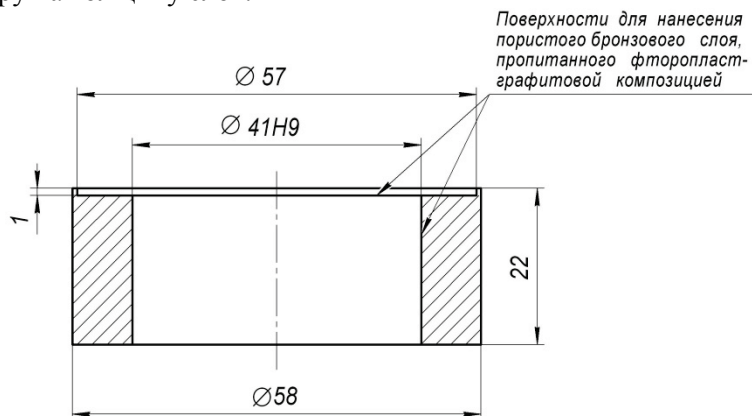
Заготовка несущей основы из бронзы БрОФ7-0,2 для изготовления спеченной втулки из материала БФГ-50М (с фланцем), аналогичной втулке 40-18-ОСТ1 10289-78 из металлофторопласта
